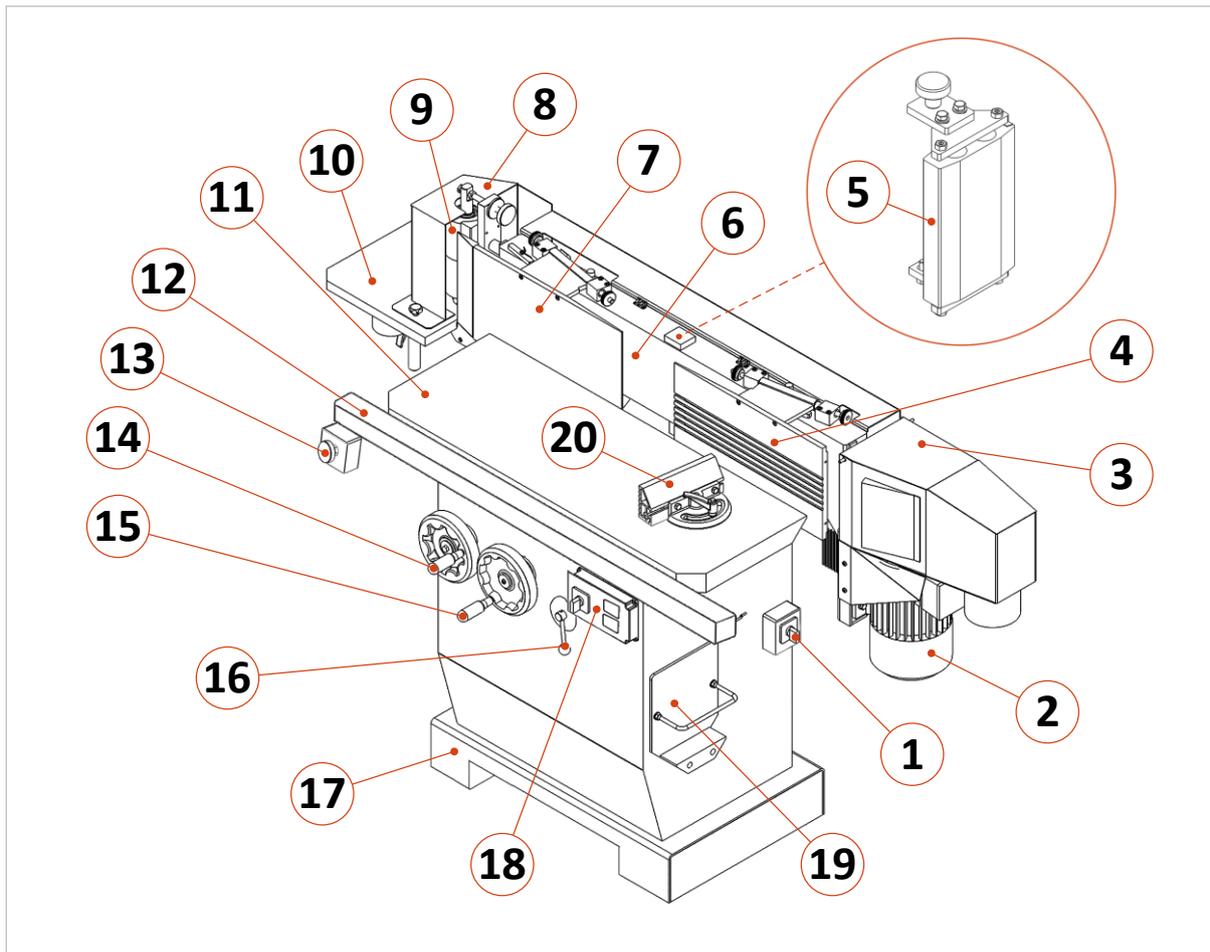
Maschinenübersicht - Hauptkomponenten
